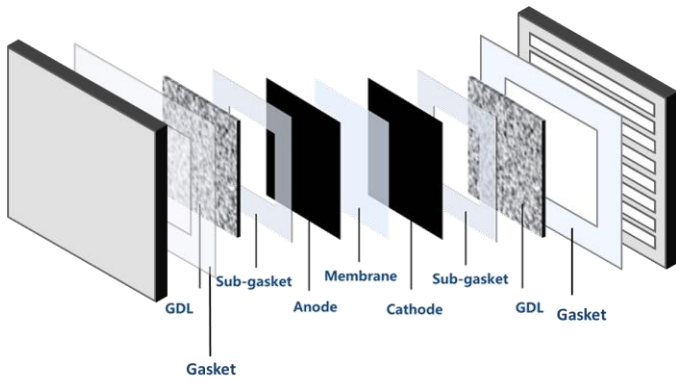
Vue éclatée d'une cellule PEM-BT à assembler (deuxième méthode d'assemblage)
